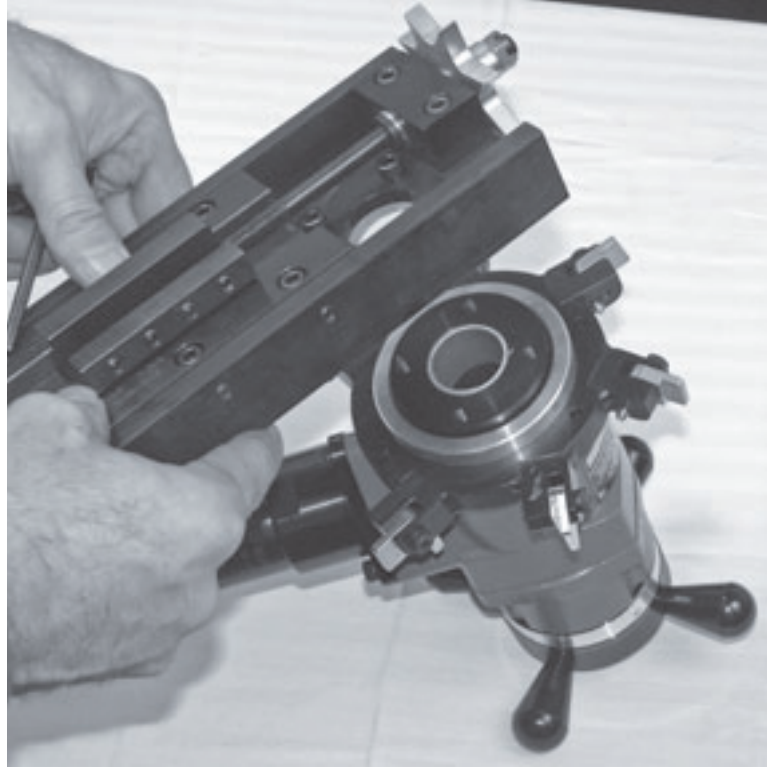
Richten Sie die Befestigungsschrauben gegenüber den Bohrungen des rotierenden Werkzeugkopfs aus.
